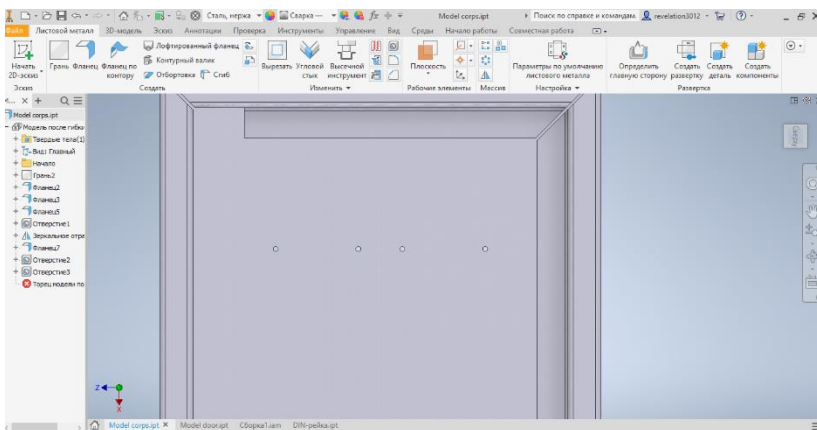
Отвори у монтажній частині корпусу щита для болтового з'єднання
